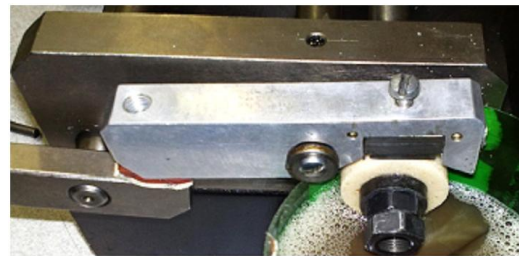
Трибометрическое устройство для оценки влияния СОЖ на процесс шлифования: 1- рычаг, 2- абразивный инструмент, 3- приспособление для фиксации, 4- заготовка.
